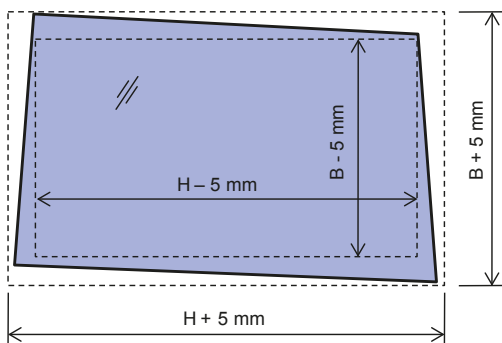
Rectangles de tolérance à largeur de fabrication et aux dimensions de fabrication
